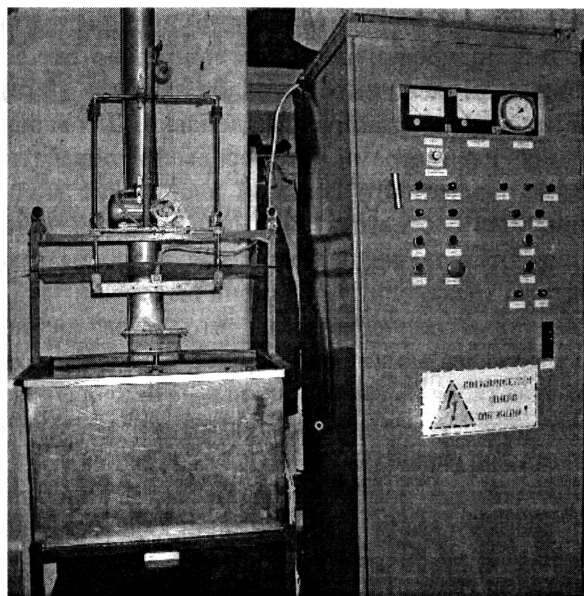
Установка ЭИП-1 для полировки малогабаритных деталей
